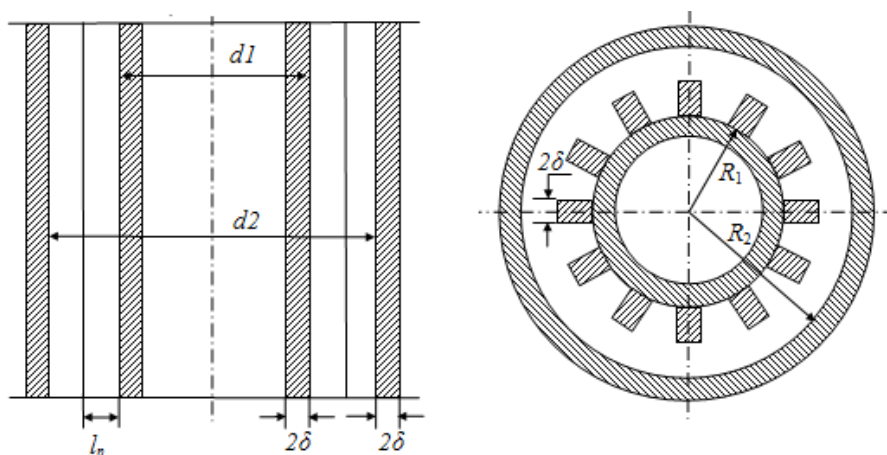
Схема ребристой теплопередающей поверхности:
